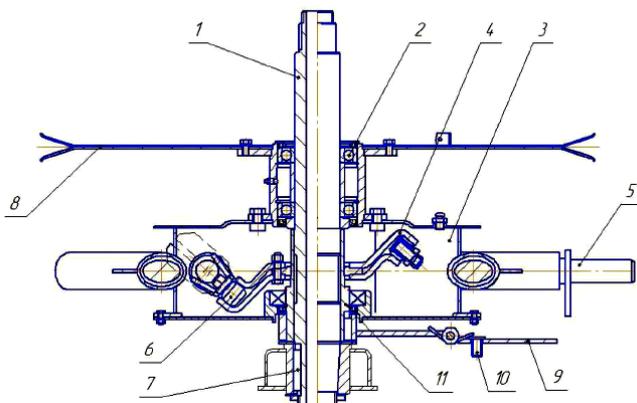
Ротор: 1 – ось; 2 – подшипник; 3 – корпус; 4 – копир; 5 – ось граблины; 6 – кулачок с роликом; 7 – шпонка; 8 – шкив; 9 – рычаг; 10 – фиксатор; 11 – втулка
